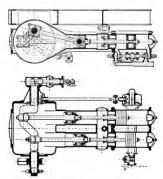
Zwillings - Dampfmaschine des Sentinell-Wagens.
